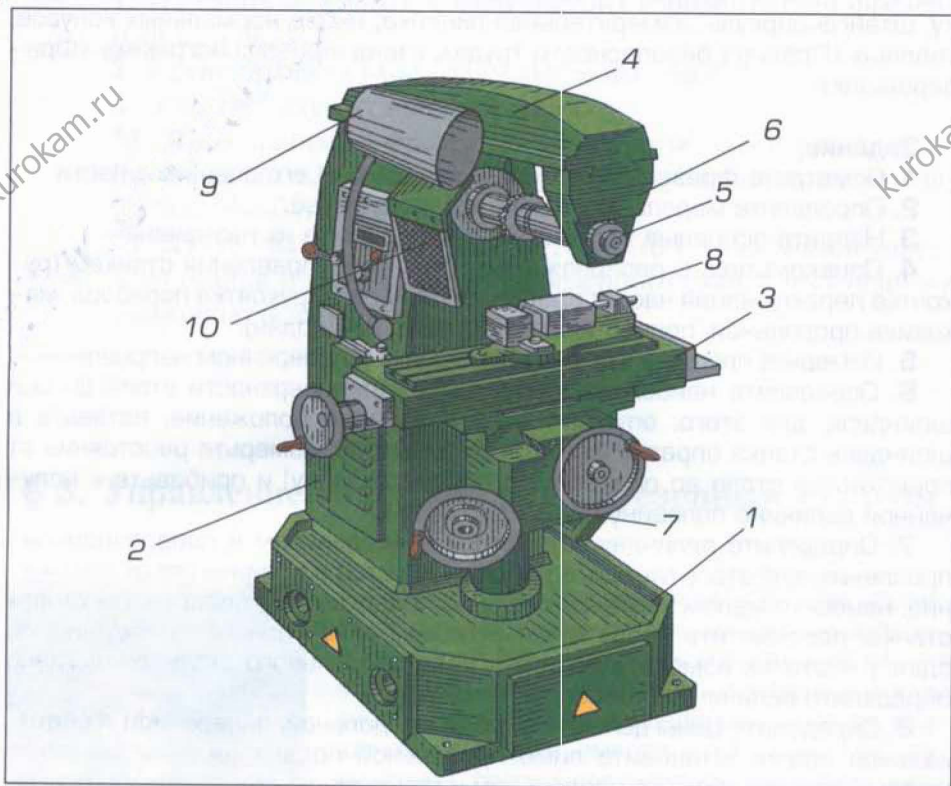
Настольный горизонтально-фрезерный станок НГФ-110-Ш4:
